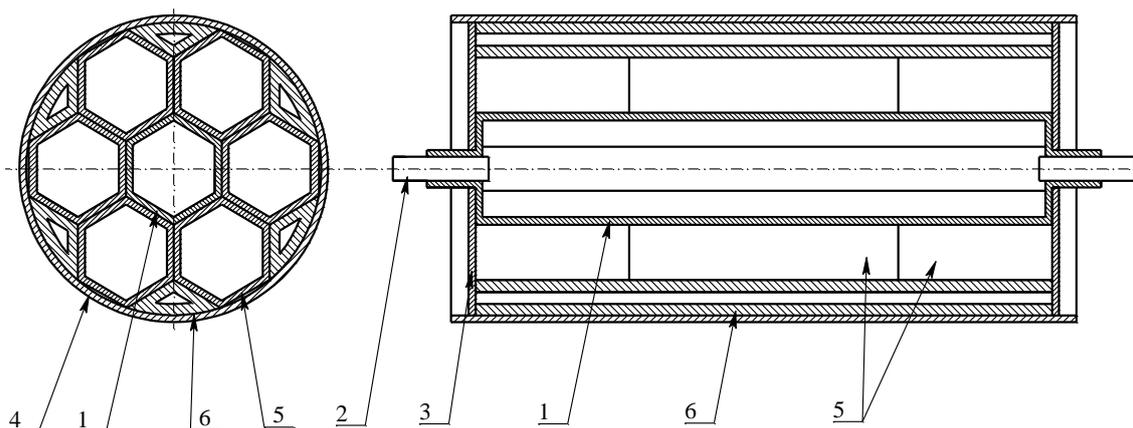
Барабан ленточного конвейера сотовой конструкции
